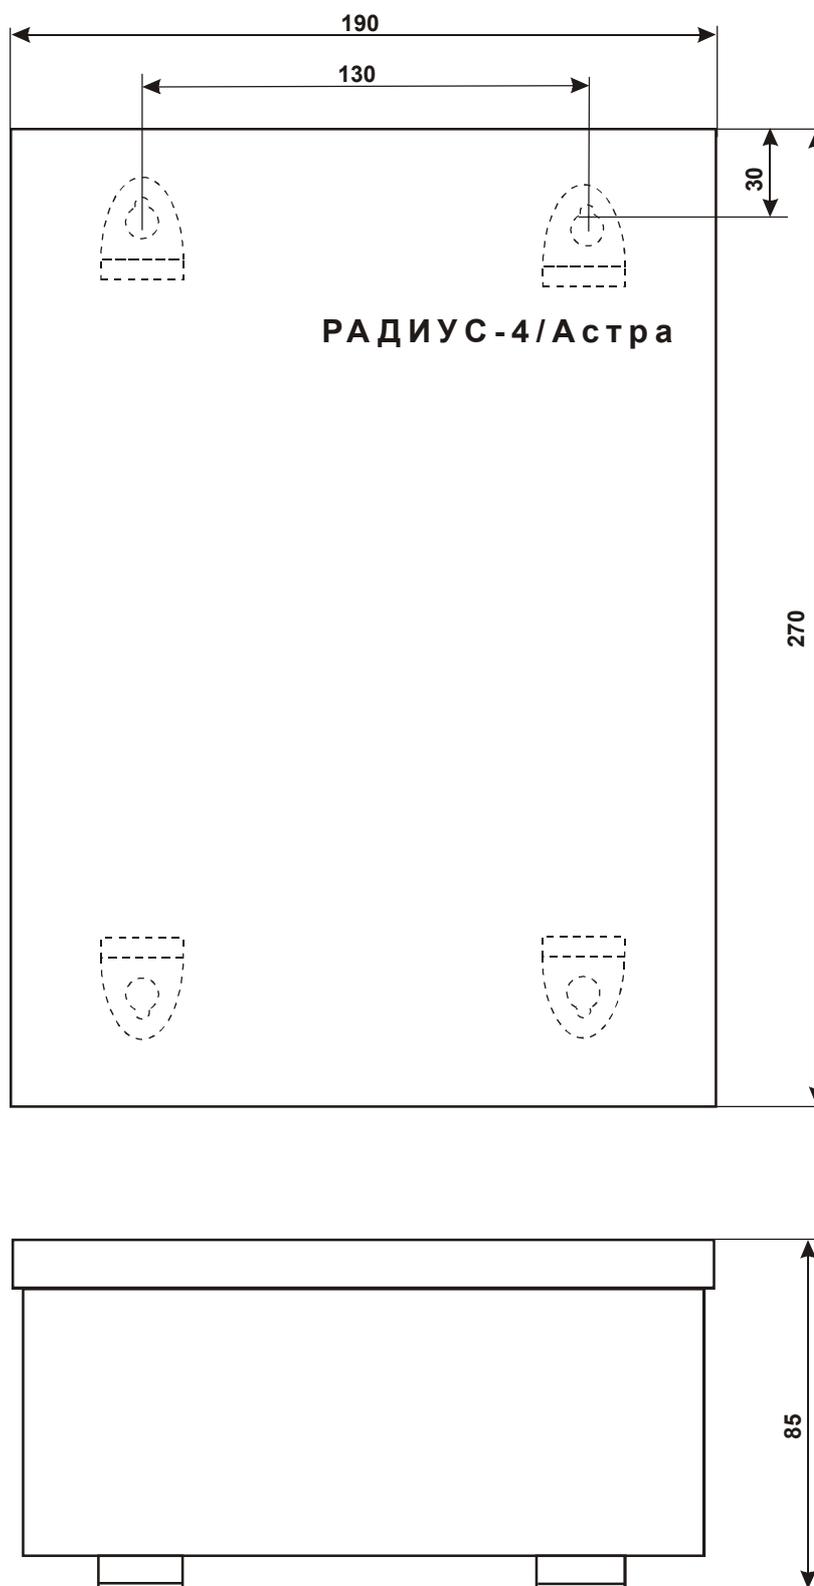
Габаритные и установочные размеры прибора «Радиус-4/Астра»
